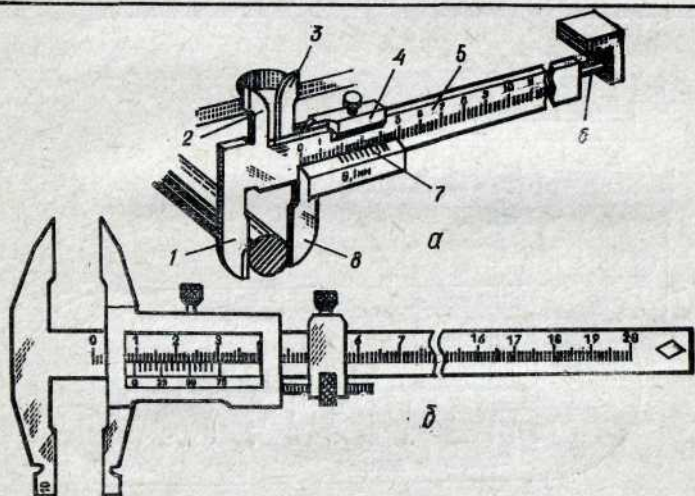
Штангенциркули: а — штангенциркуль ШЦ-I (1, 2 — неподвижные губки; 3, 8 — подвижные губки; 4 — подвижная рамка; 5 — штанга; 6 — глубиномер; 7 — нониус); б — штангенциркуль ШЦ-II для измерения и разметки.
